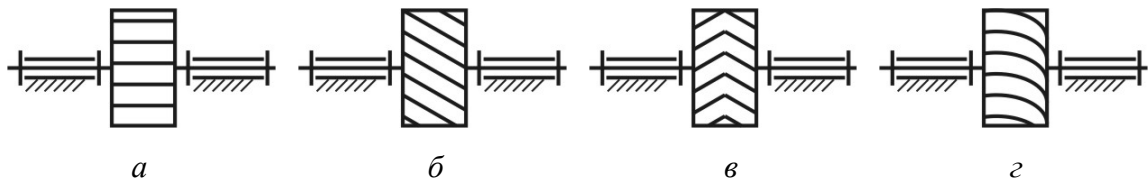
Расположение зубьев на ободе колеса: *a* – прямозубые; *б* – косозубые; *в* – шевронные; *г* – с круговыми зубьями
